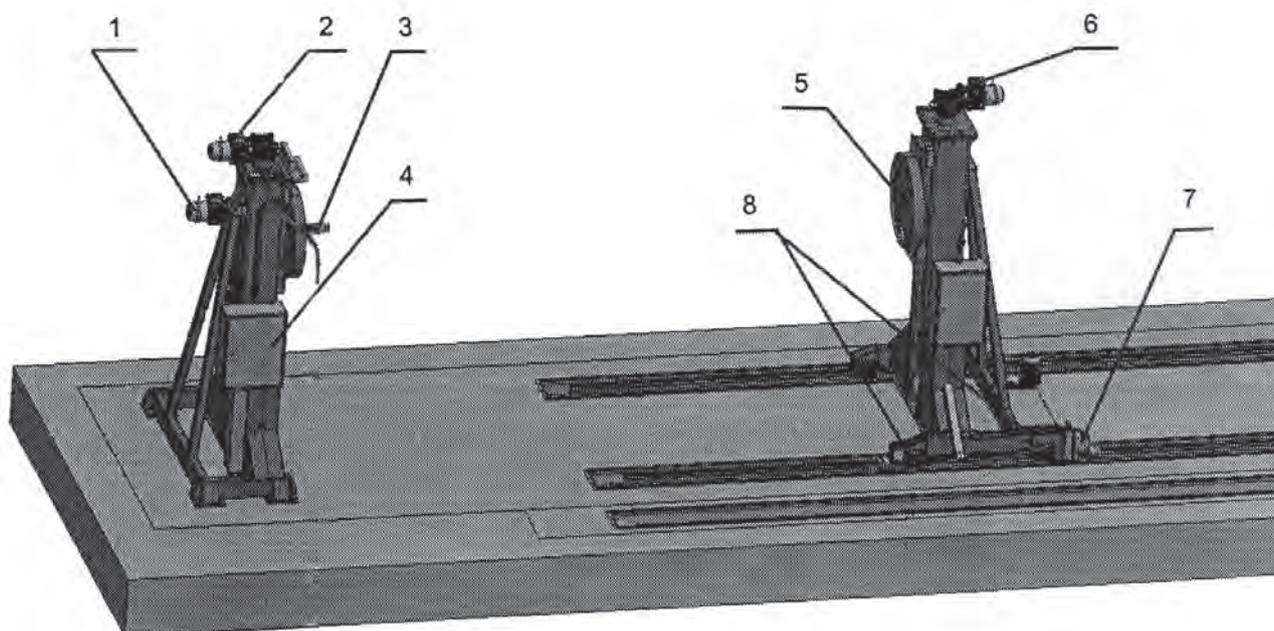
Внешний вид кантователя грузоподъемностью 10 т: 1 – привод поворотного механизма; 2 – привод вертикального перемещения поворотного механизма неподвижной колонны; 3 – ведущий поворотный механизм; 4 – пульт управления; 5 – ведомый поворотный механизм; 6 – привод вертикального перемещения поворотного механизма подвижной колонны; 7 – механизм фиксации колонны; 8 – ролики
